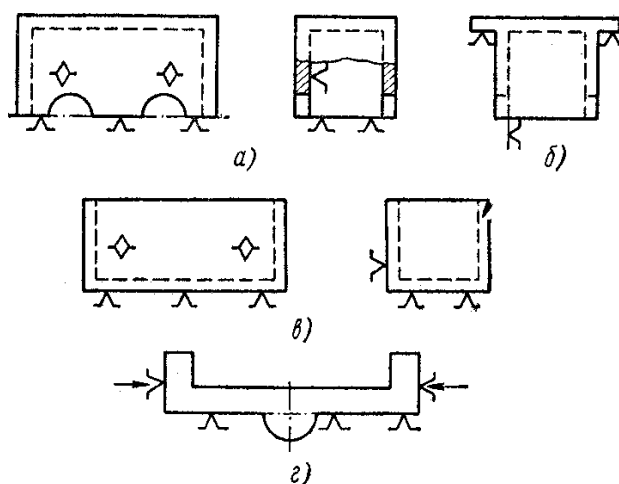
Схема базування корпусних деталей на першій операції по необроблюваних плоских поверхнях
